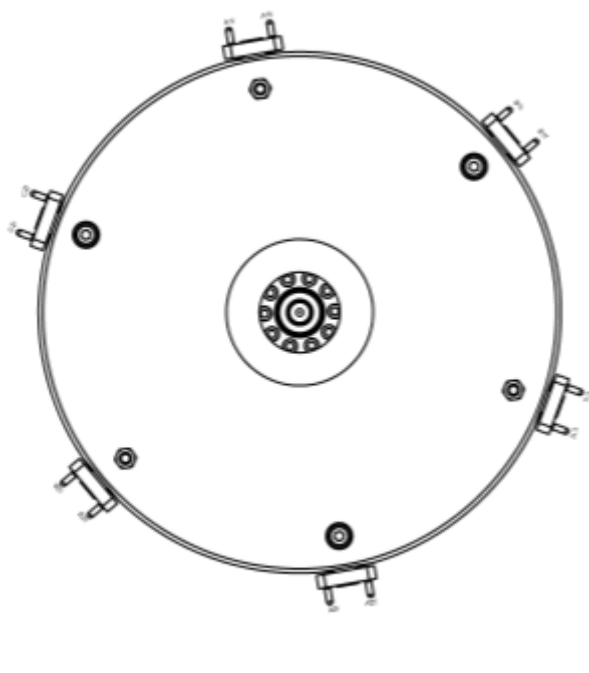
vista statore assemblato con i terminali di connessione per le sei bobine
